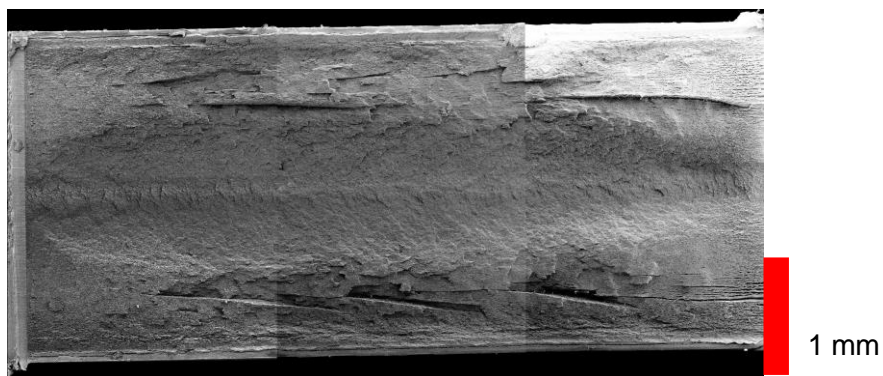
Imatge composta de la superfície de fractura de Bioblend 0 zona central
